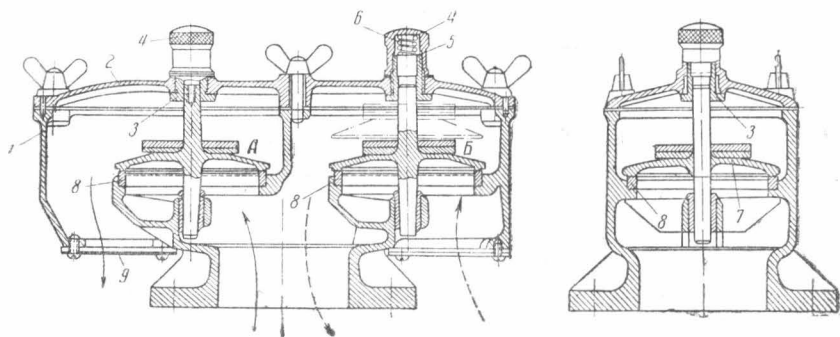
Дыхательный клапан с горизонтальным расположением тарелок:
